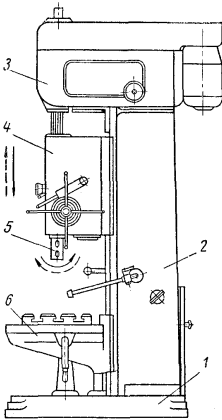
Вертикально-свердлильний верстат: 1 – фундаментна плита; 2 – станина; 3 – коробка передач; 4 – коробка подачі і механізм подачі; 5 – шпиндель; 6 – стіл
